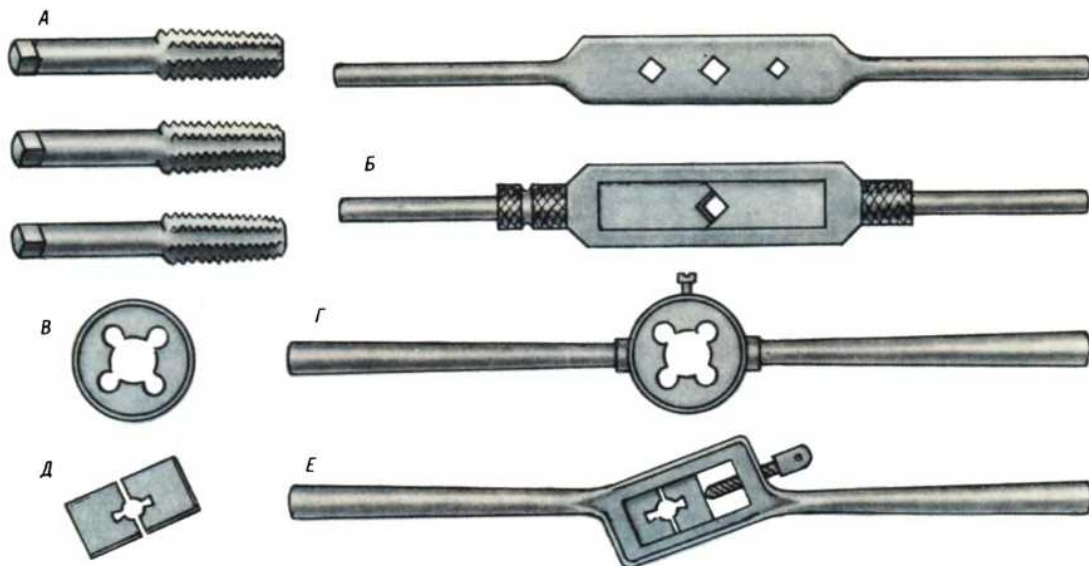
Болтонарезной и гайконарезной инструмент: А — метчики; Б — воротки; В — круглая плашка (лерка); Г — вороток; Д — плашка раздвижная; Е — клупп.
